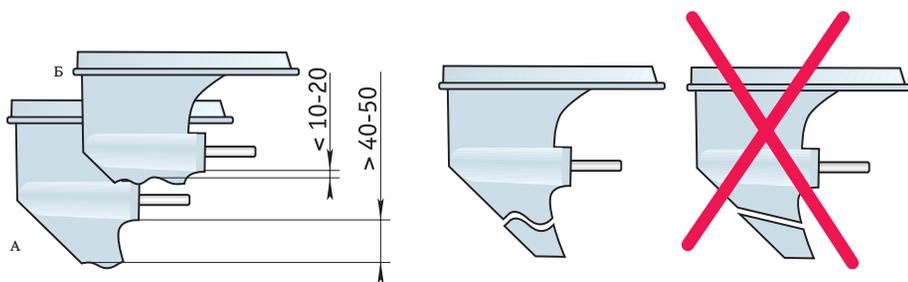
В «простых» случаях (А) разборка редуктора перед сваркой не требуется; если перо обломано под самый корень (Б), необходимо использовать оправку-«холодильник»
